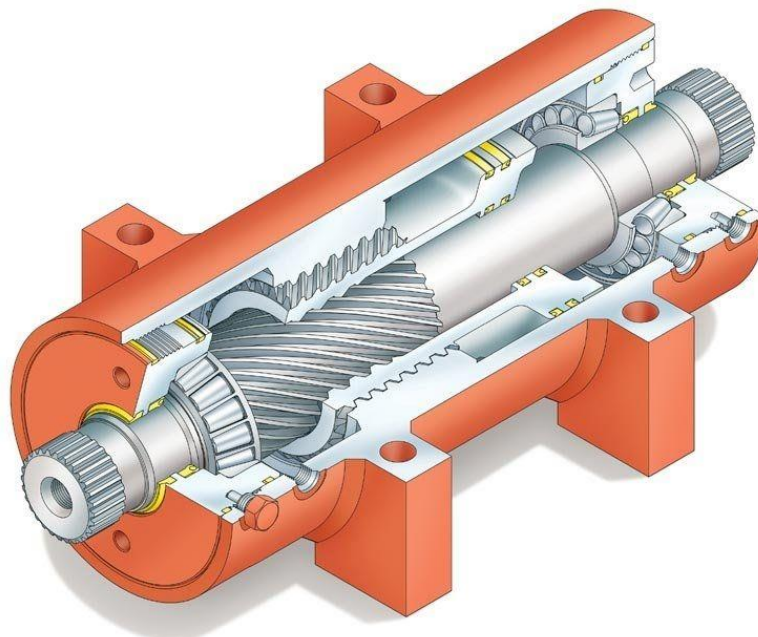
Rotační dělič firmy Hunger Maschinen [15]
